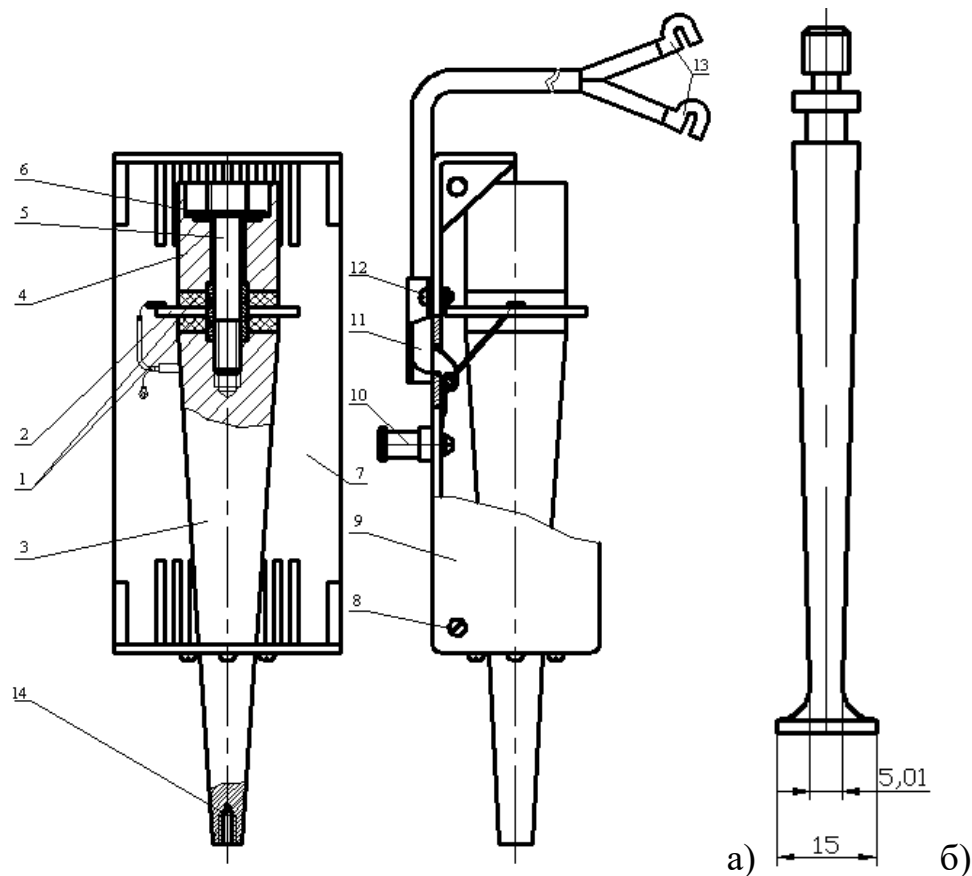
Будова випромінювача установки УЗДН-А: а) конструкція концентратора: 1 – п'єзокерамічні кільця; 2 – пластина-контакт; 3 – концентратор; 4 – хвостовик; 5 – болт; 6 – шайба; 7 – корпус; 8 – гвинти; 9 – захисна кришка; 10 – штир; 11 – кабель живлення; 12 – накладка; 13 – клеми; 14 – різьба для закріплення робочих насадок; б) конічна насадка.
